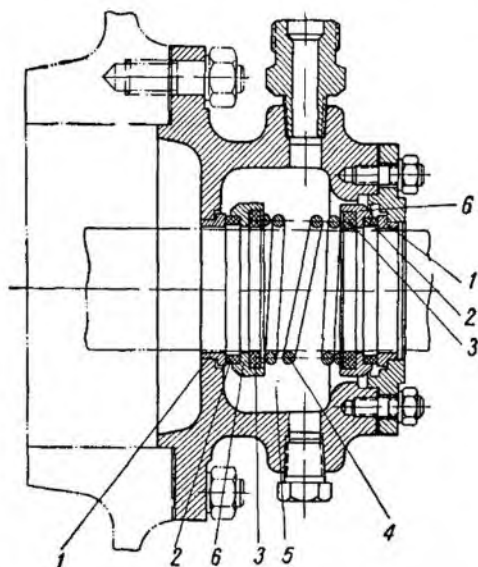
Самоустанавливающийся сальник: 1 — неподвижное стальное кольцо; 2 — графитовое кольцо; 3 — кольцо из маслбензостойкой резины; 4 — пружина; 5 — масляная камера; 6 — обойма
